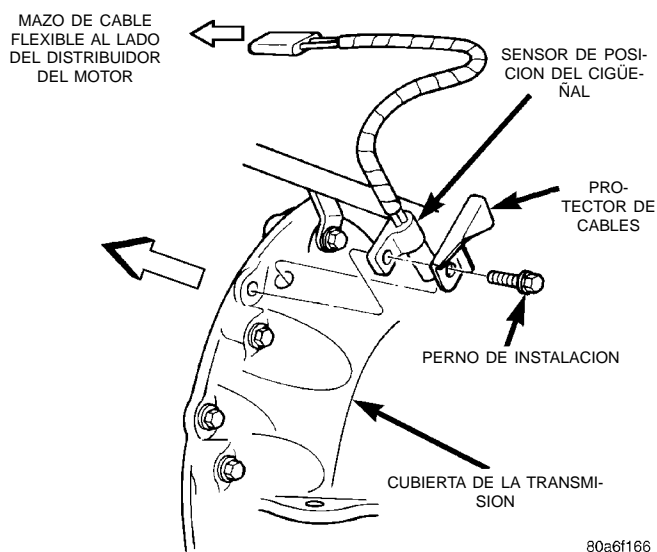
Sensor de posición del cigüeñal—Motor 4.0L y 6 cilindros
